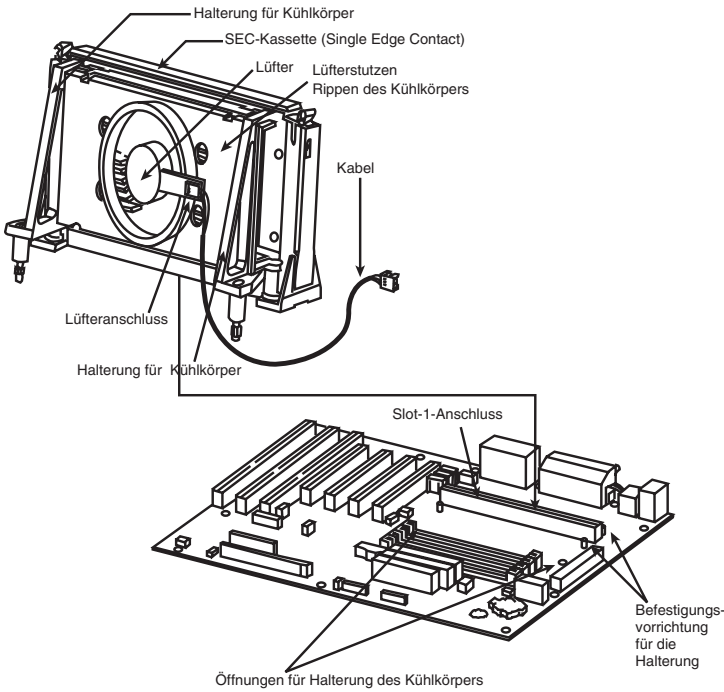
Pentium-II-Prozessor mit Kühlvorrichtung
